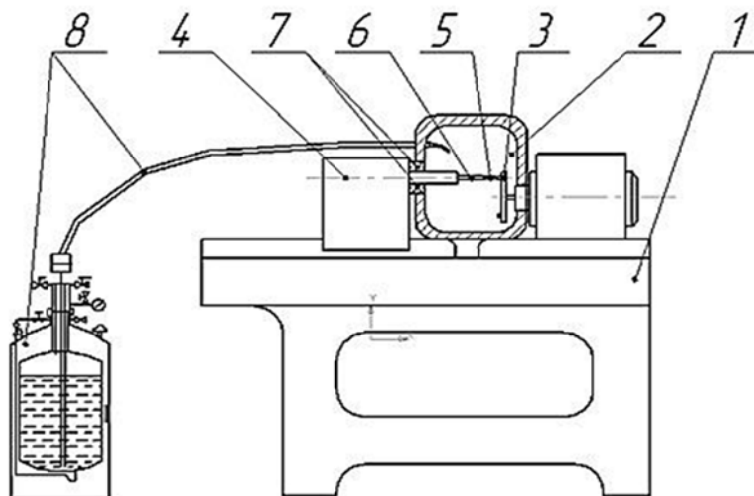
Установка для получения порошка высокоскоростным способом (1 – рама; 2 – камера для сборки; 3 – шлифовальный круг; 4 – устройство подачи; 5 – заготовка; 6 – оправа; 7 – защитные элементы; 8 – устройство подачи жидкого азота в зону обработки)
